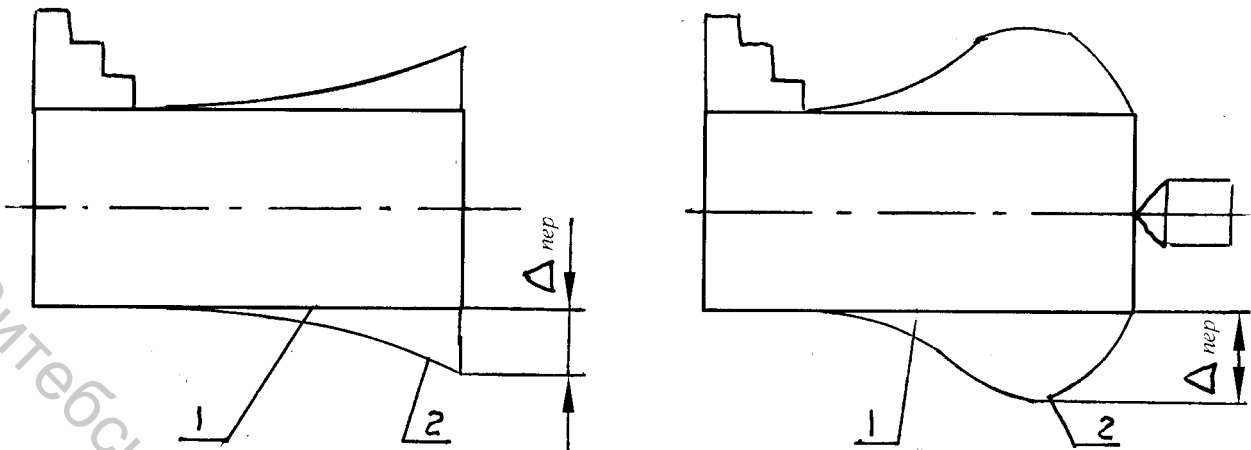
Схемы образования погрешности при закреплении заготовки в трехкулачковом патроне
